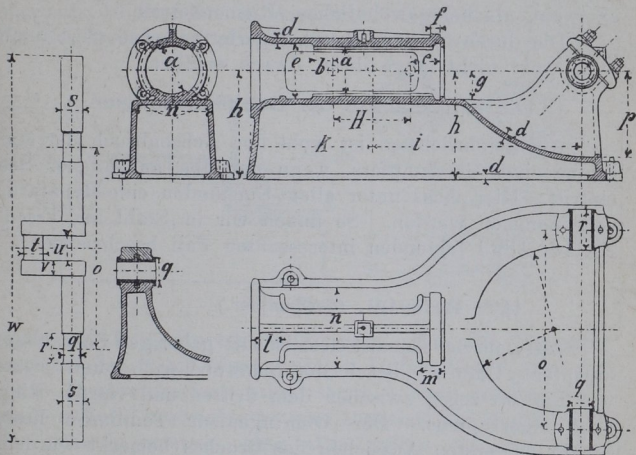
64. Dampfmaschine mit gekröpfter Welle.
